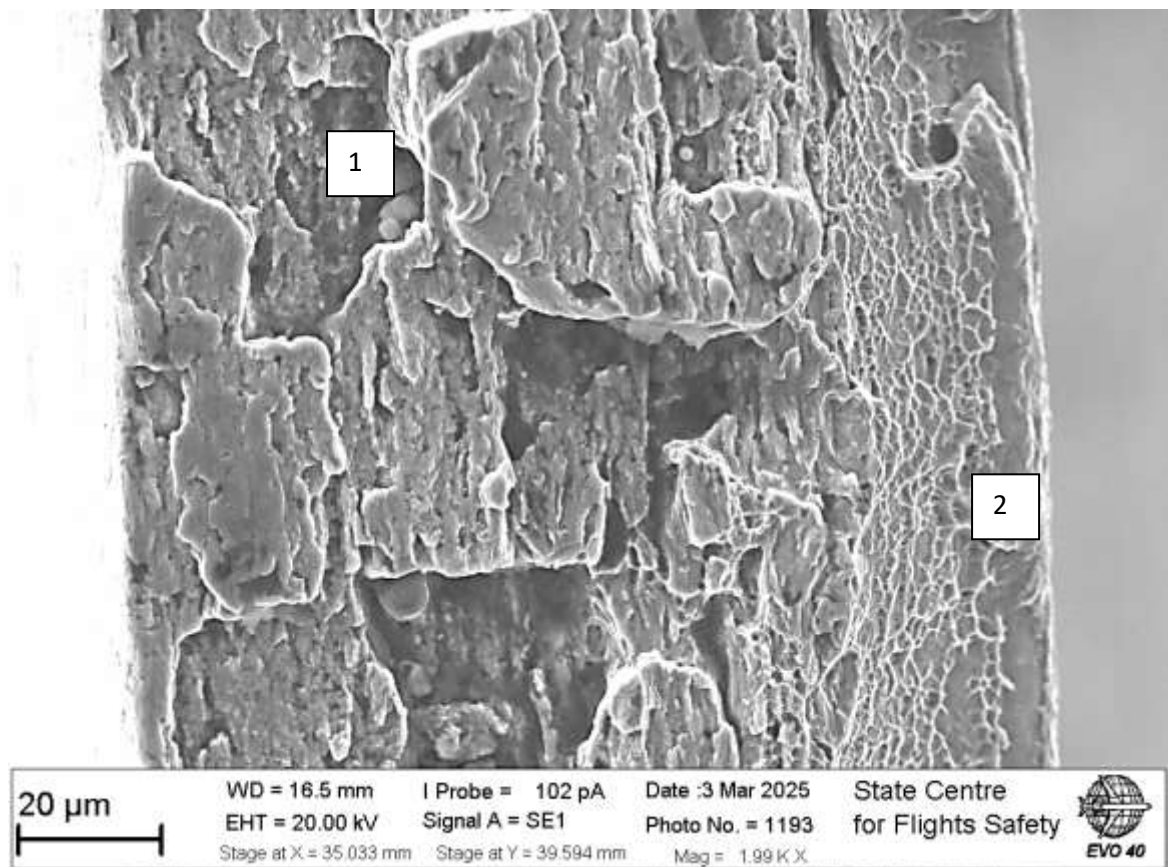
Вид двух зон излома «1» и «2» с разной шероховатостью.
